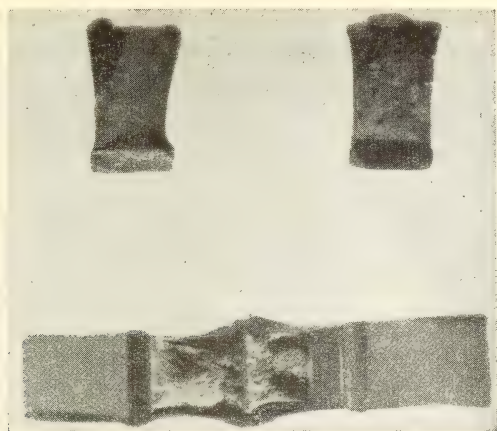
Probeta de acero dúctil fracturada por impacto Charpy con velocidad media (*Autor*).
